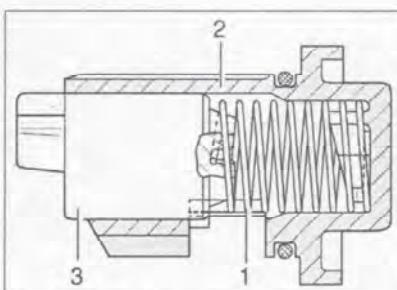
Сборка механизма блокировки передачи заднего хода.
